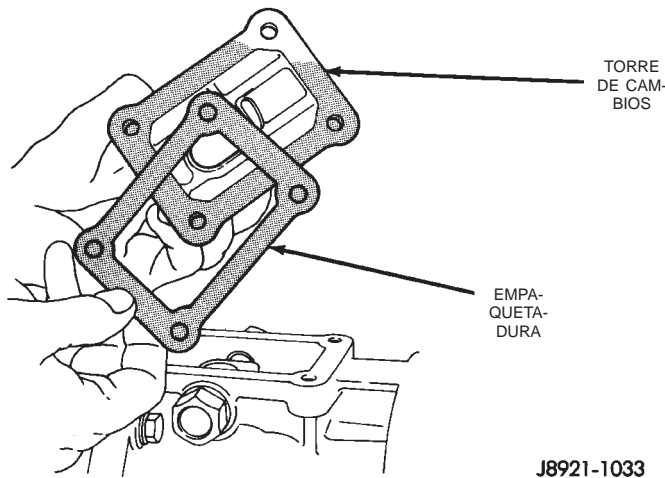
Desmontaje de la empaquetadura de la torre de cambios
